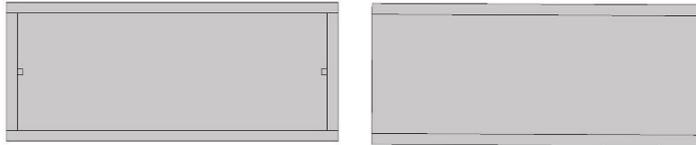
ALZADO Y PERFIL CAJONERA 600
